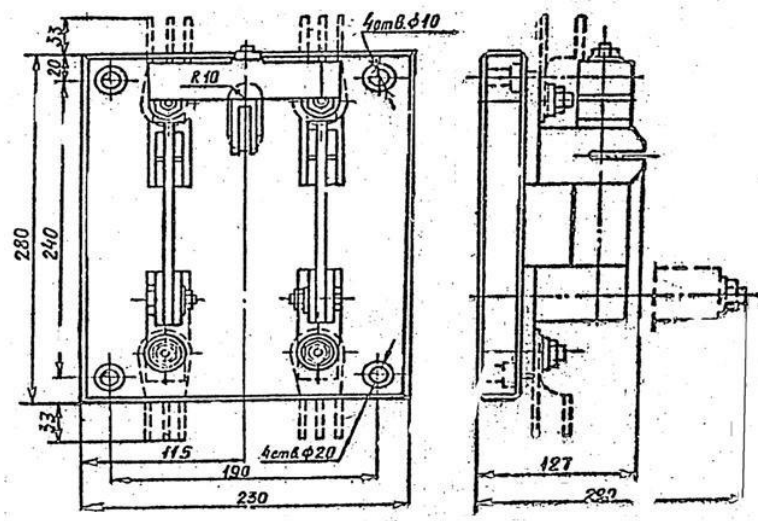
Разъединитель ГВ-22АУЗ.
